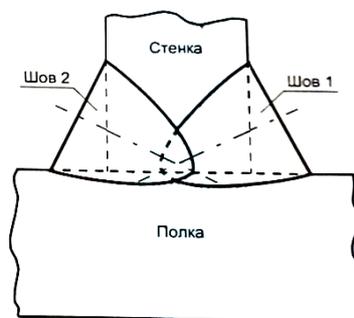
Схема таврового сварного соединения с полным проваром соединяемых деталей
